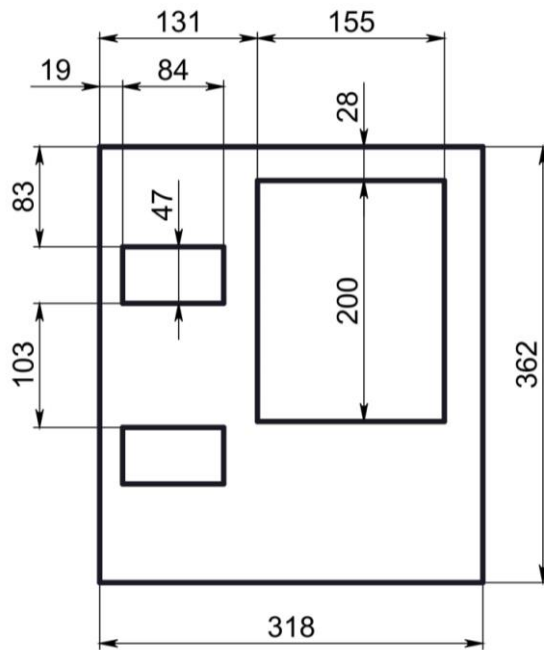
Габаритные, установочные и присоединительные размеры
